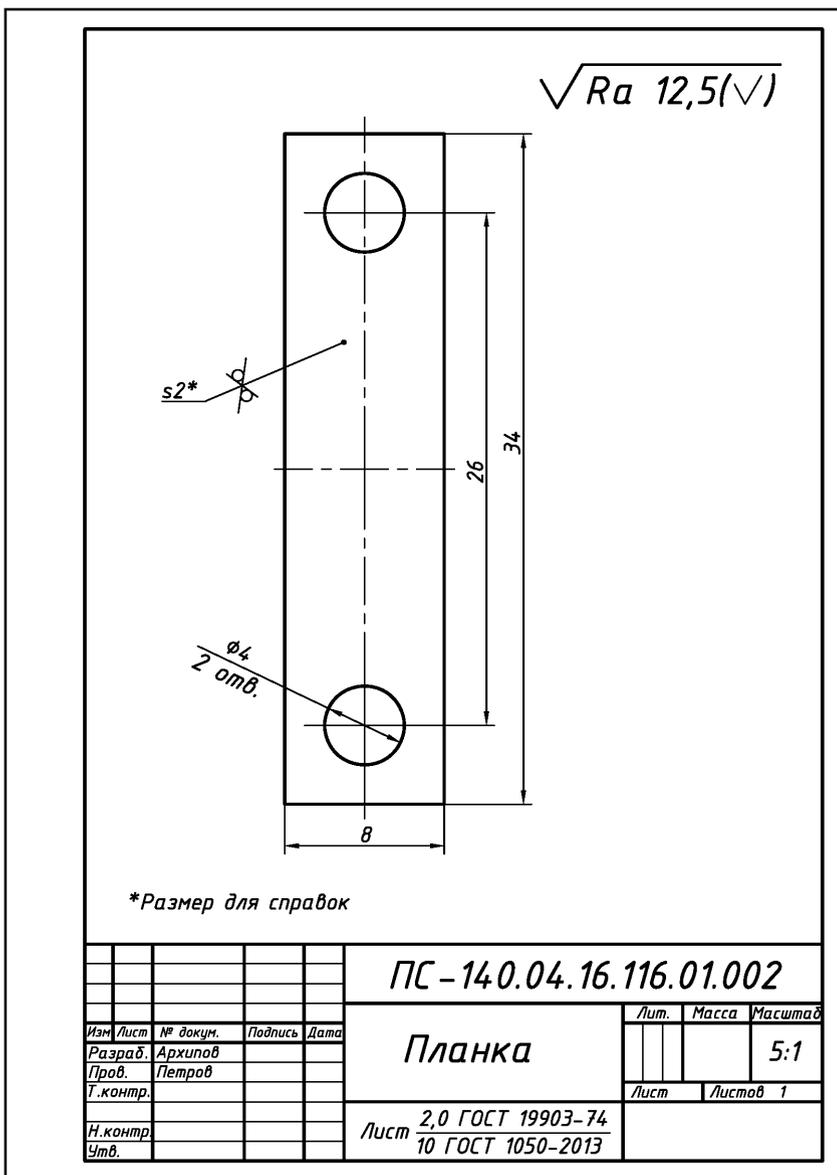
Оформление рабочего чертежа детали «Планка»
